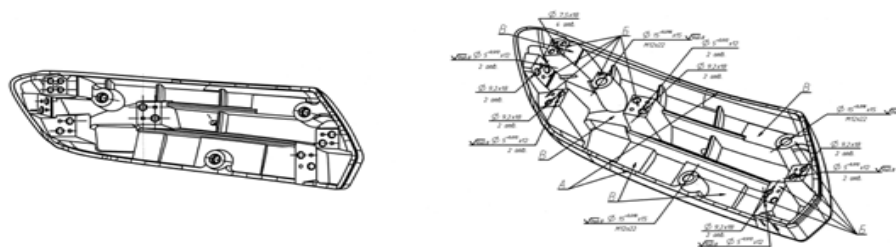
Эскиз калибра, изготовленного методом литья алюминия и механической обработкой
